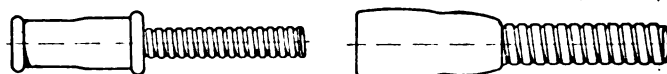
u. 49. Gummimuffen für Gasschläuche.
